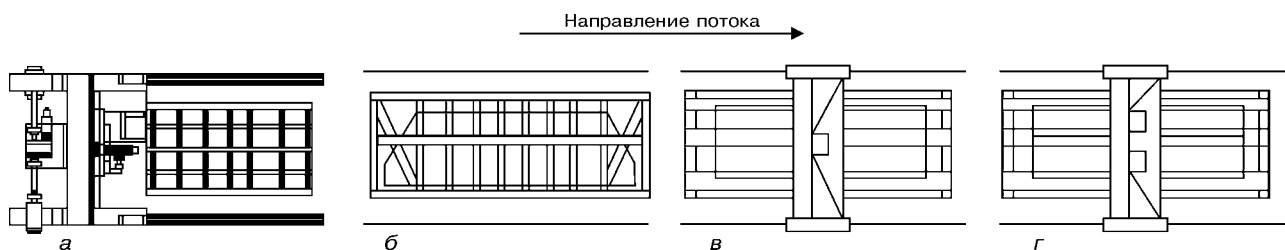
Схема поточной линии сборки и сварки боковой стены вагона-минераловоза: а — установка сборки и сварки полотна обшивки; б — стенд сборки каркаса боковой стены с полотном; в — установка ДТС полотна с каркасом; г — установка автоматической сварки полотна с обвязками
